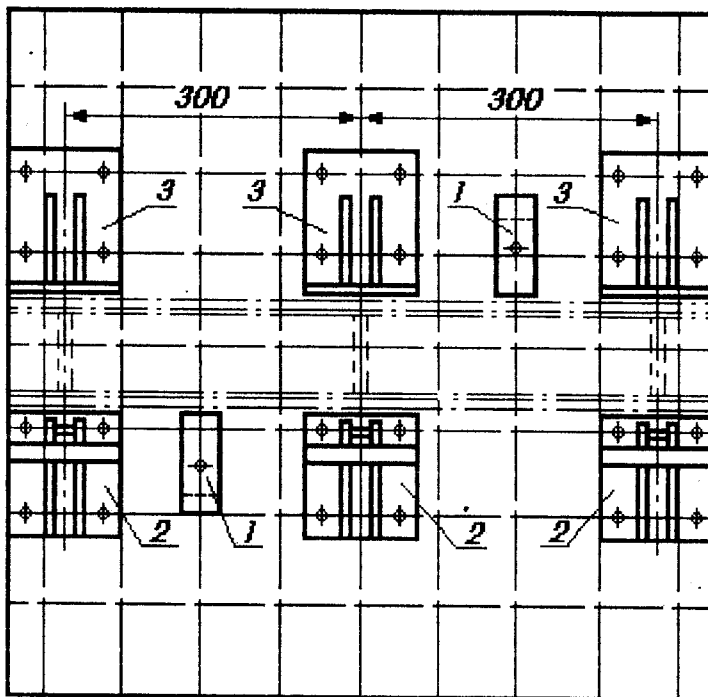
Схема настройки плиты для сборки коробчатой балки
